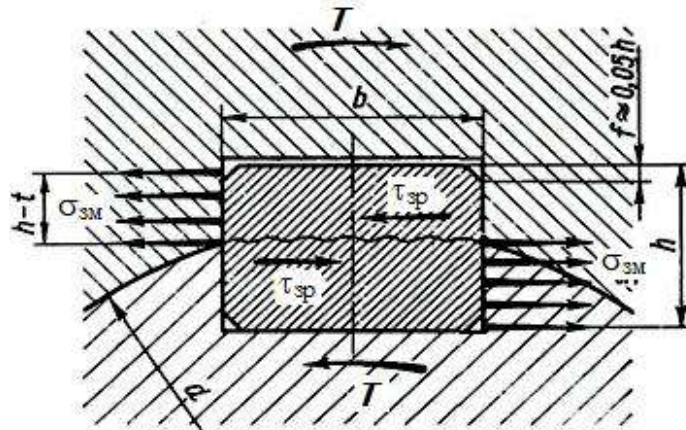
Розрахункова схема з'єднання призматичною шпонкою
